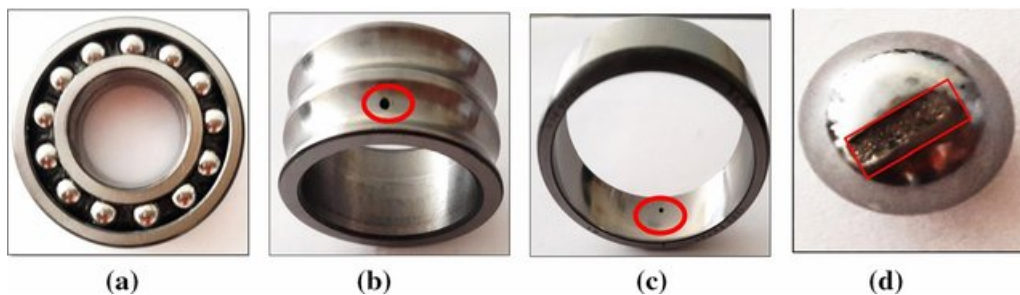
Roulement sain (b) défaut de la bague intérieure (c) défaut de la bague extérieure (d) défaut de la bille [38].
